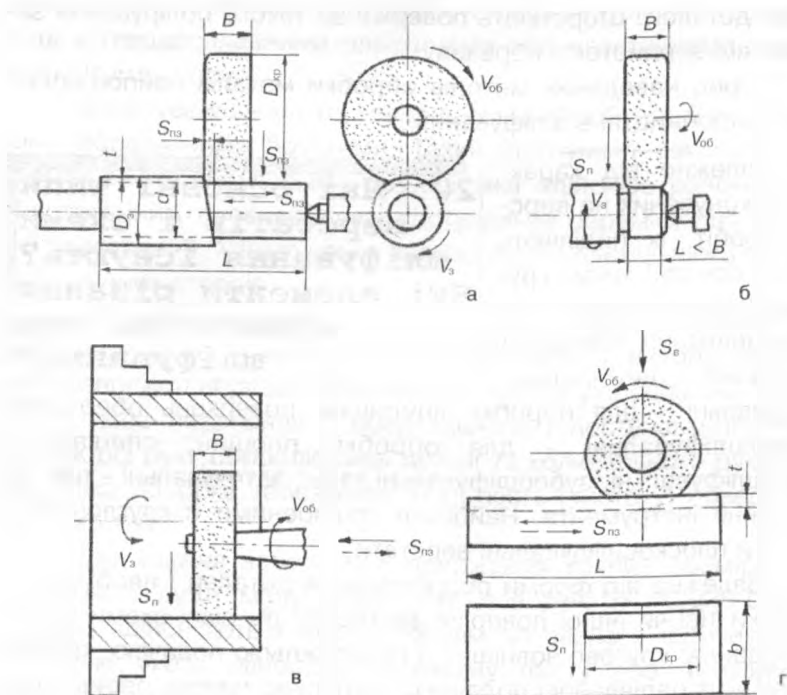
Схеми кругового (а-в) і плоского (г) шліфування: B - ширина шліфувально круга, $D_{кр}$ - діаметр шліфувального круга, D_z - діаметр заготовки до обробки, d - діаметр заготовки після обробки, b - ширина плоскої заготовки
